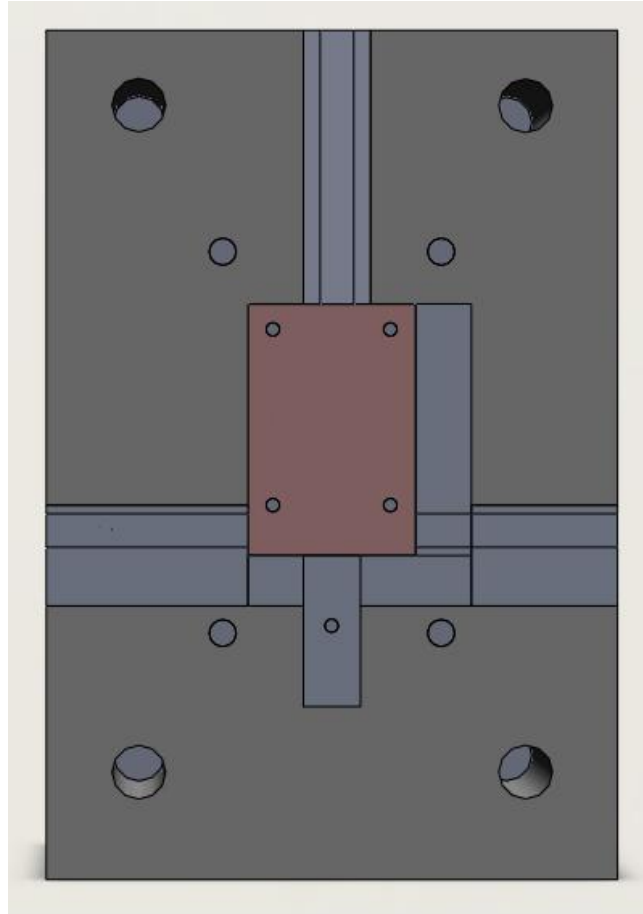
Vista en planta de la configuración de llenado central largo.
